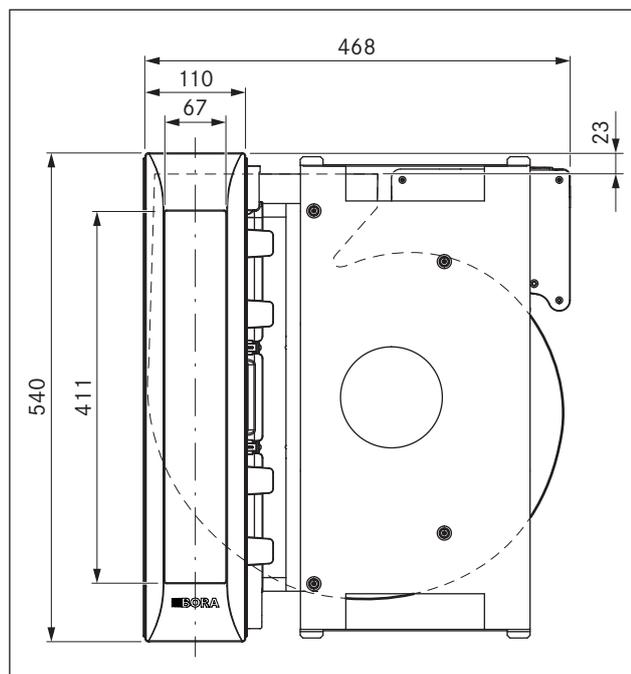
PKAS, PKASAB dimensiones del aparato vista en planta
